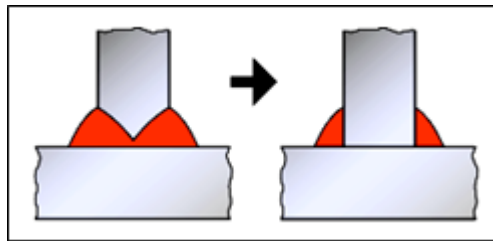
Configuration du Joint la soudure à deux angles. [12]
